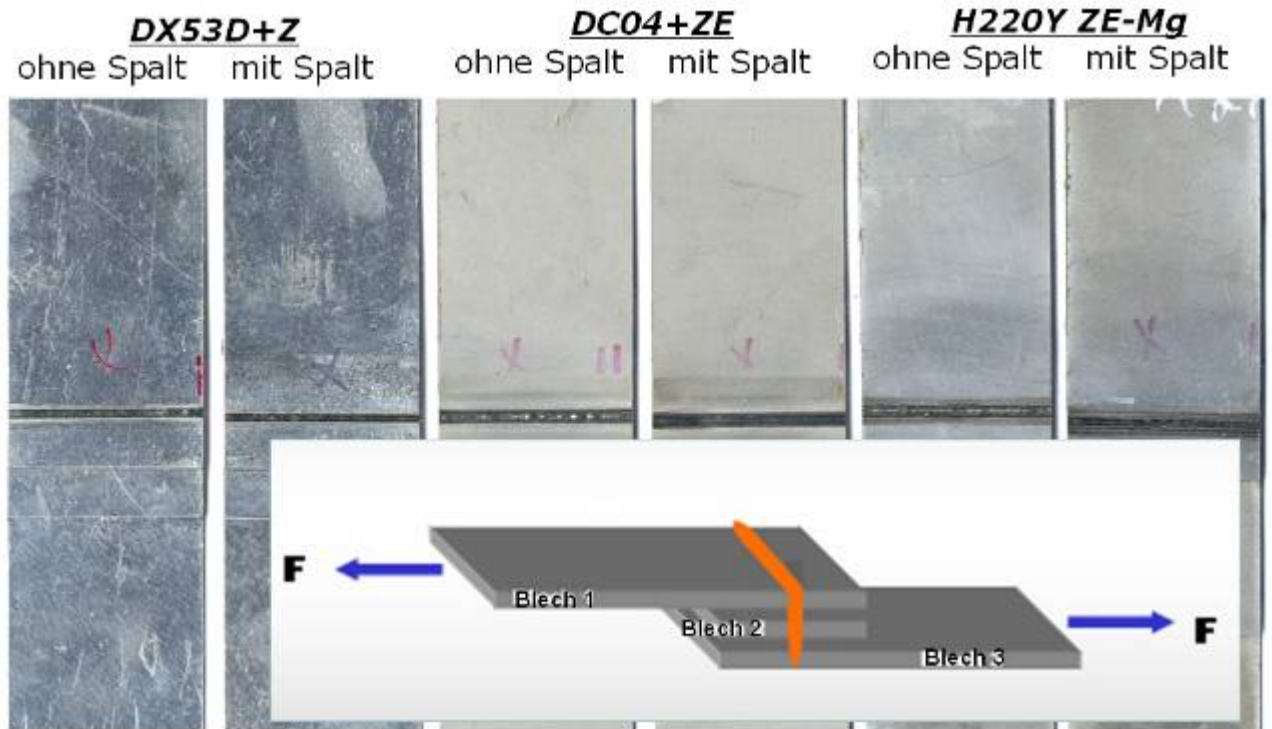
Ausgewählte Zugproben und Schema der Zugproben
